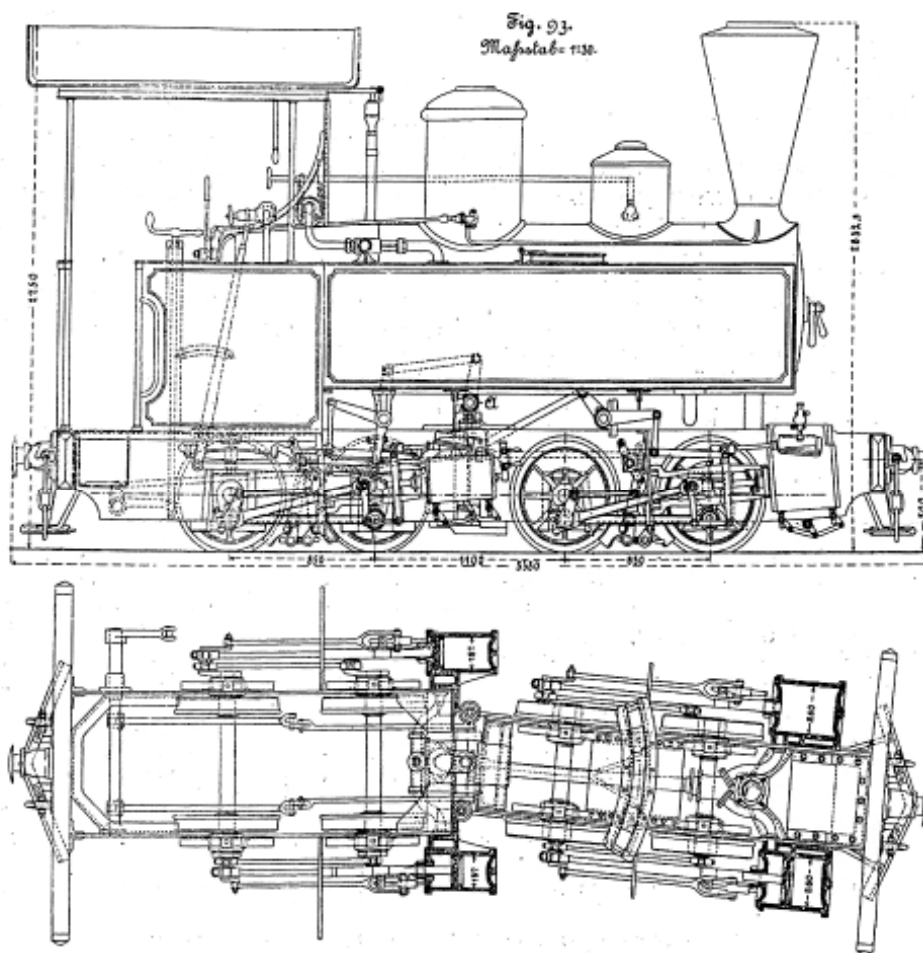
Gen. Plan der ersten Mallet-Gelenk-Lok, 1888 (Salomon (1890))
